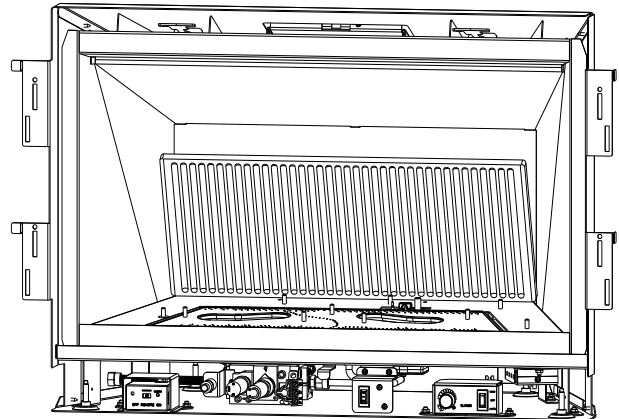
Installer le panneau arrière. Panneau cannelé illustré.
